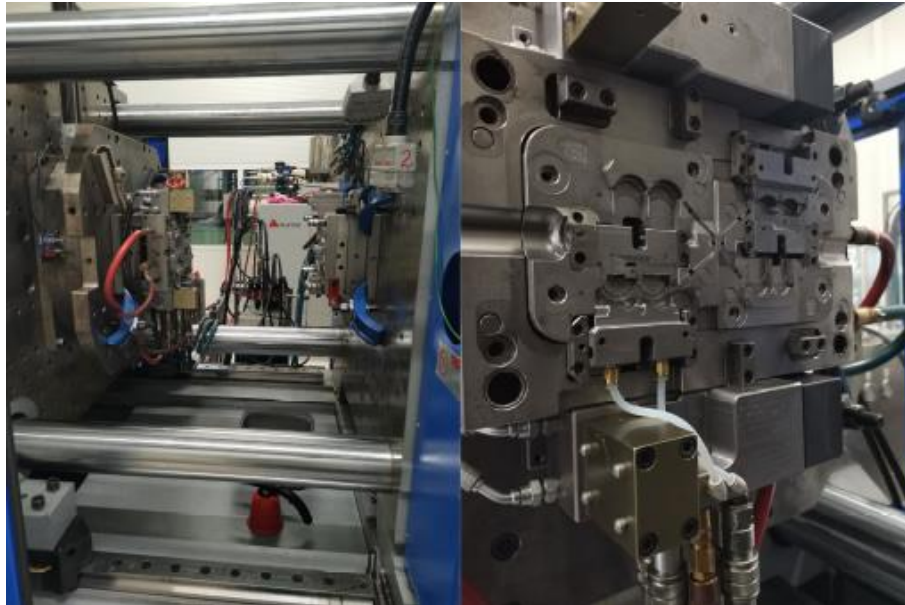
(izquierda) máquina de moldeo por inyección con molde ensamblado; (derecha) detalle de la cavidad del molde que muestra el inserto L-PBF con entradas de enfriamiento.
